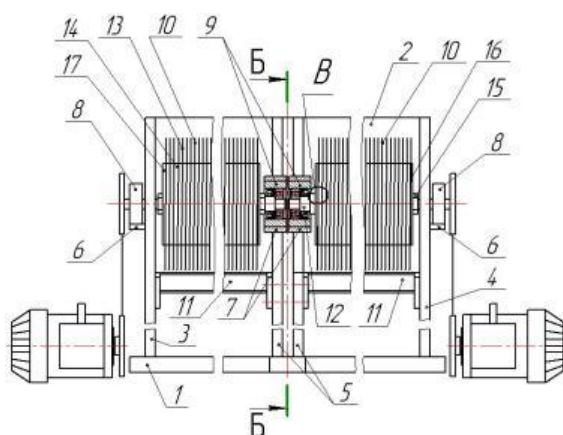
Принципиальная схема конструкции волокноочистителя. 1-рама; 2-корпус волокноочистителя; 3-4- крайние стенки; 5- средняя стенка перегородка; 6 и 7-опоры; 8 и 9 корпуса подшипников; 10- пильный цилиндр; 11-колосники; 12- пильные валы; 13-пилы; 14-междупильная прокладка; 15-затяжные гайки; 16-косая шайба; 17-шпонка; 18-электродвигатель.
